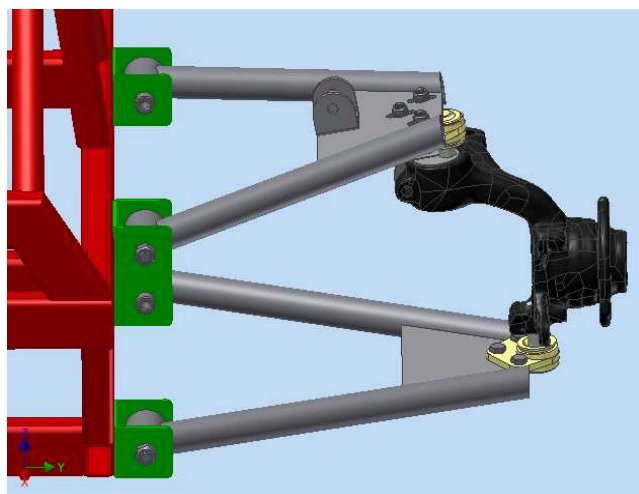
Navržené horní rameno zavěšení zadních kol se silentbloky
